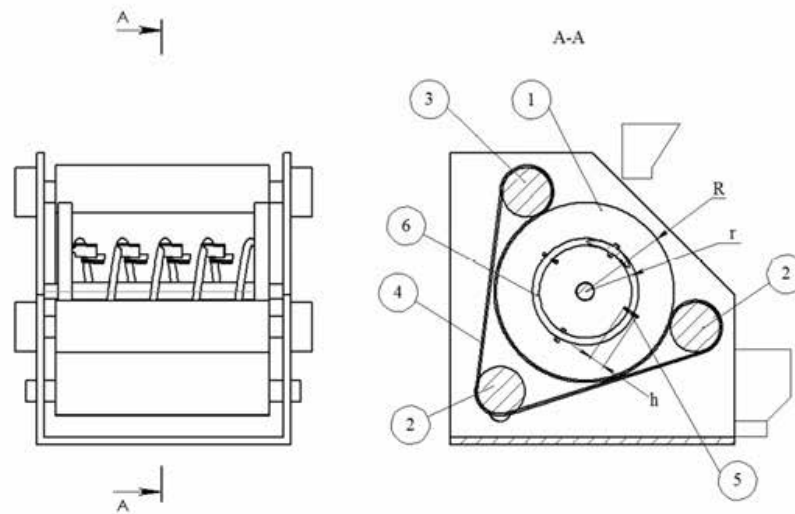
Принципова схема змішувача з допоміжними лопатями
